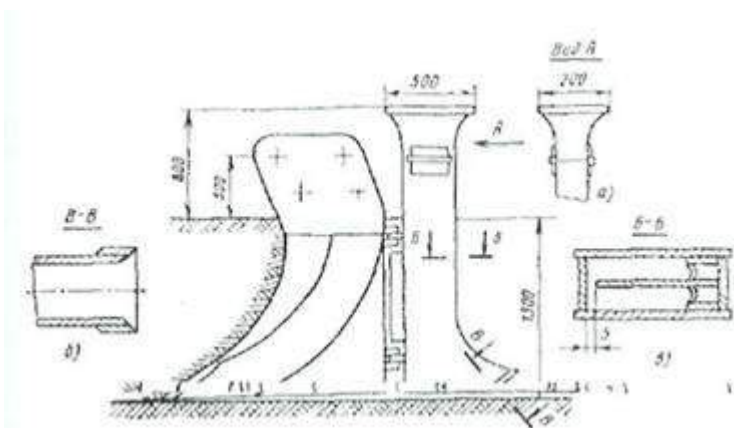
Кассета для прокладки кабеля с наружной пластмассовой оболочкой
